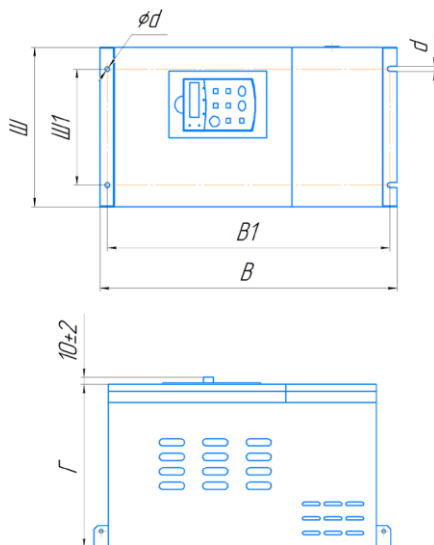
б Габаритные и установочные размеры устройств серии LCI в пластмассовом корпусе
